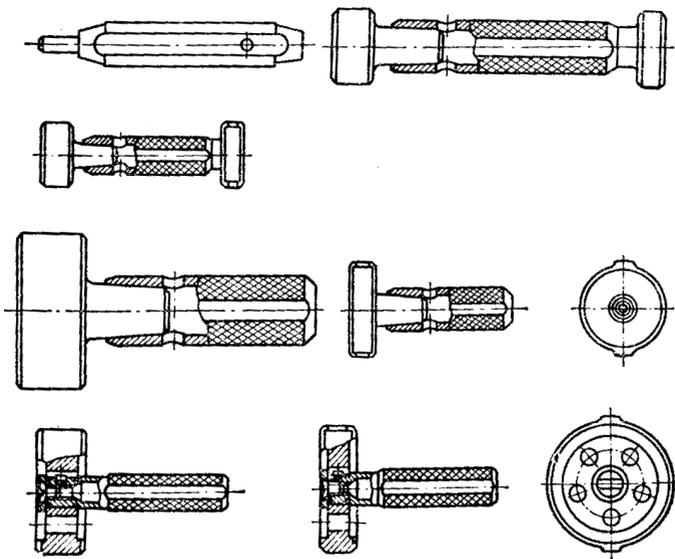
Гладкие калибры-пробки и их конструкции
